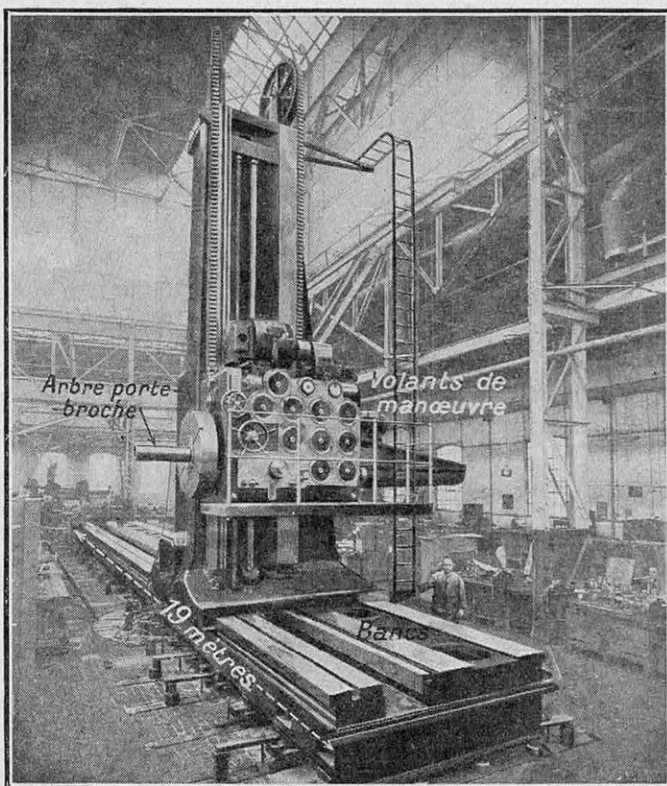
MACHINE GÉANTE A FRAISER ET A ALÉSER HORIZONTALE
